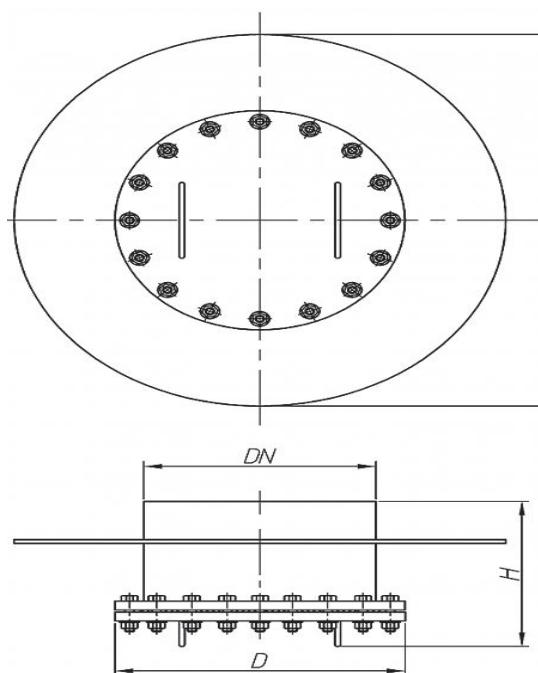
Люк-лаз круглый без поворотного устройства
